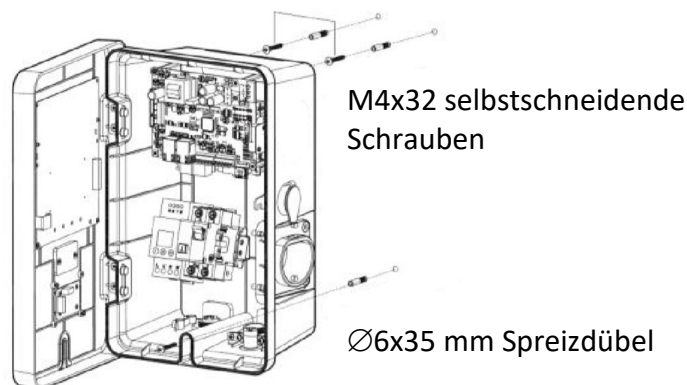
Positionierung der Schrauben für die Wandbefestigung
